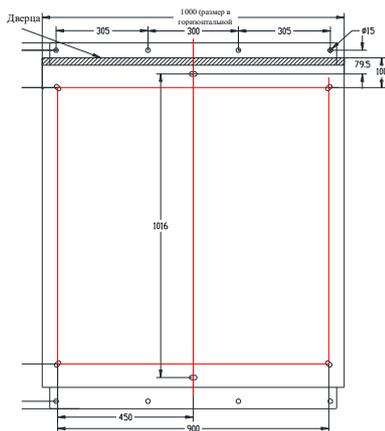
Установочный чертеж сейсмозащитных устройств с размерами
